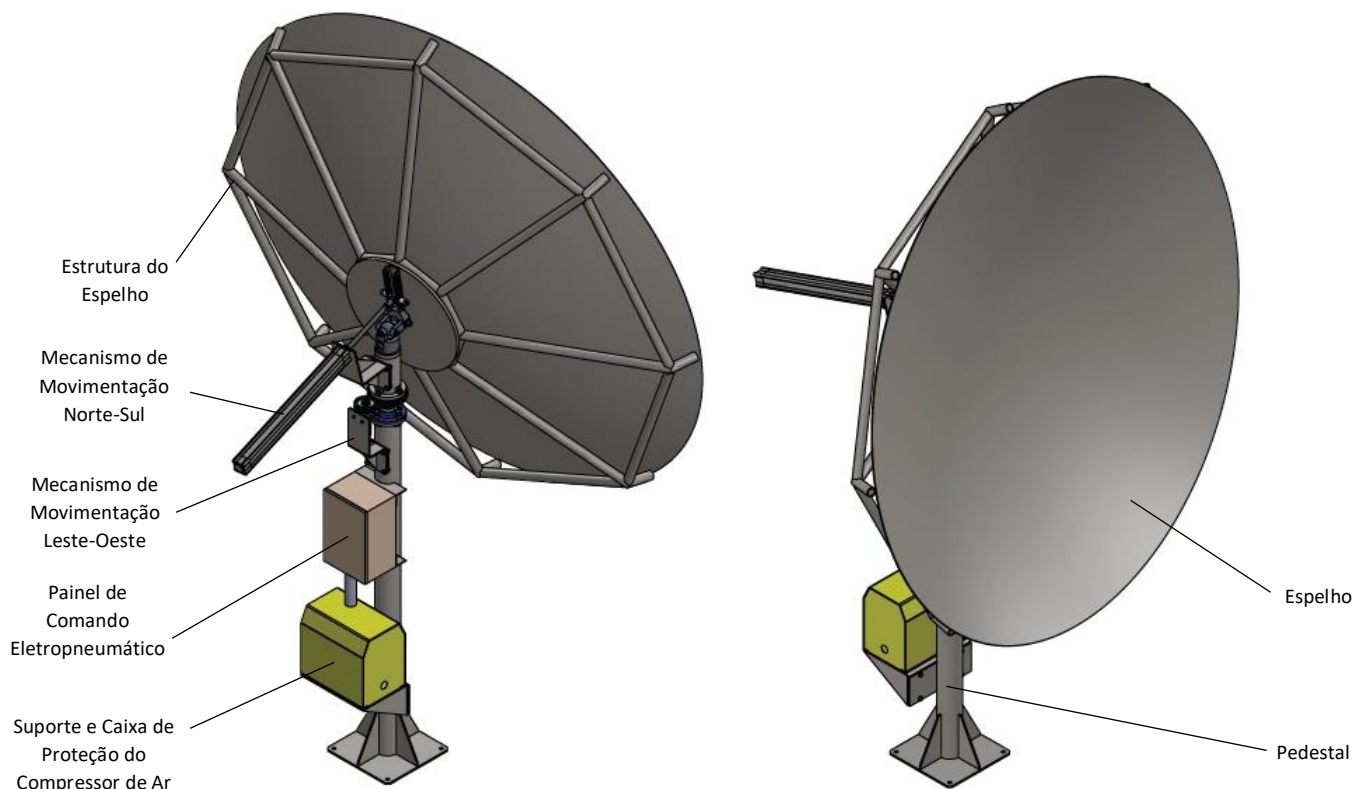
À esquerda: vista Isométrica privilegiando a parte traseira do heliostato; À direita: vista isométrica privilegiando a parte frontal do heliostato – fonte: o autor
